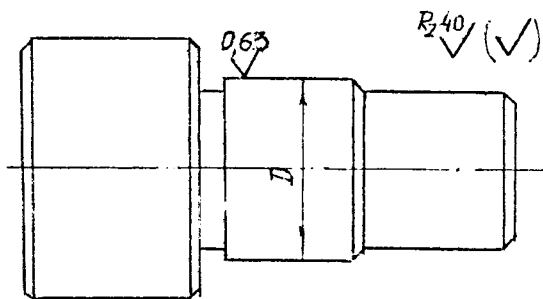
Вал ступенчатый. (Материал - группа стали М1 или М2; заготовка - штамповка на ГМ)
